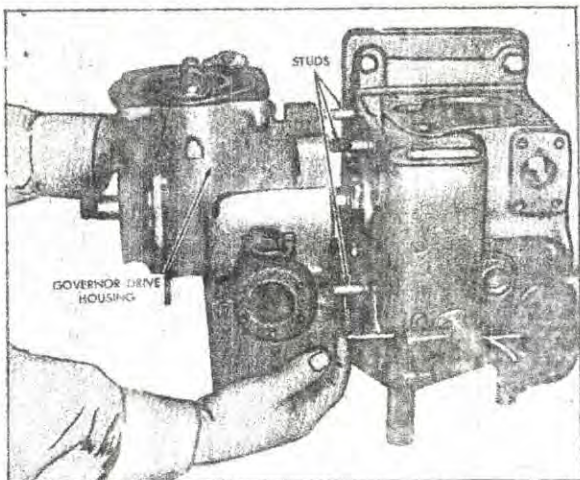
Desmontaje del conjunto del regulador mecánico.
